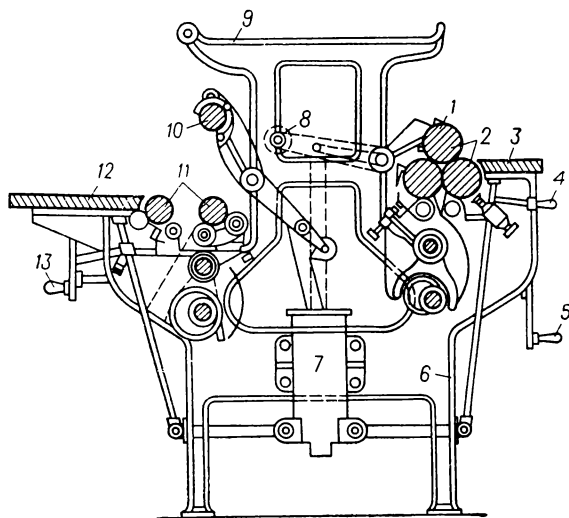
Рукавсоборочная машина (поперечный разрез):
